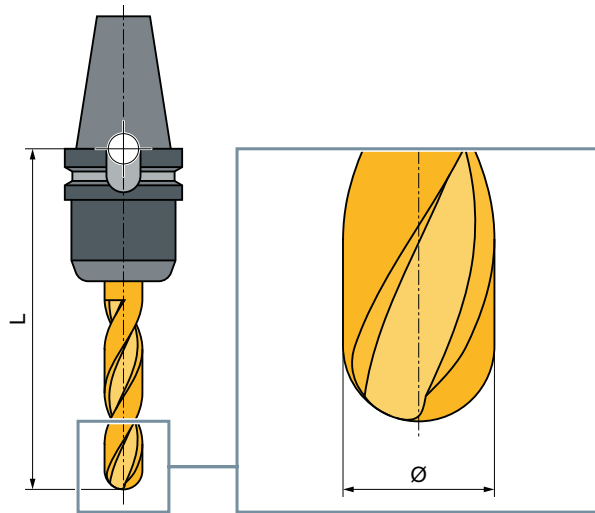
3D-Werkzeug am Beispiel eines zylindrischen Gesenkfräasers (Typ 110)
